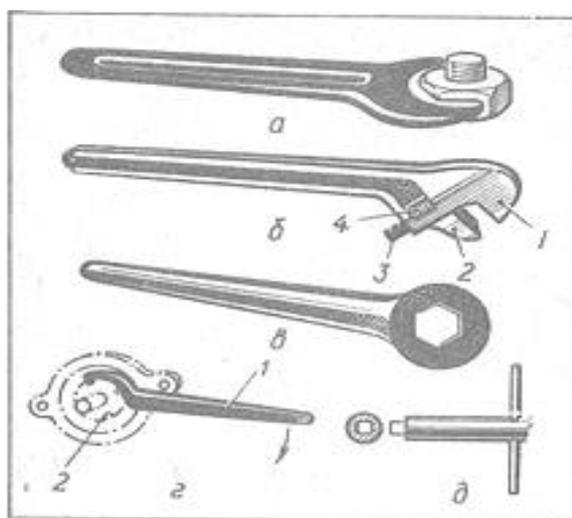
Гаечные ключи: а — односторонний открытый; б — раздвижной с червячным винтом (1 — неподвижная губка; 2 — подвижная губка; 3 — зубчатая рейка; 4 —
